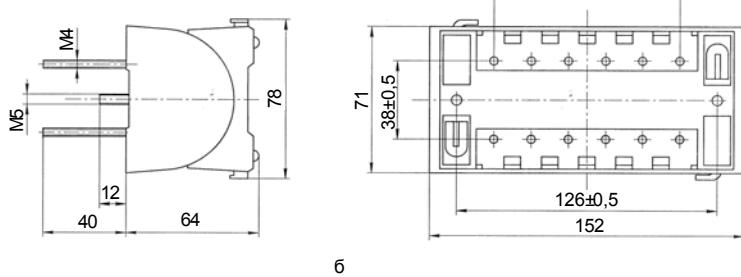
Габаритные размеры крышки холостой типа КХ 4.
